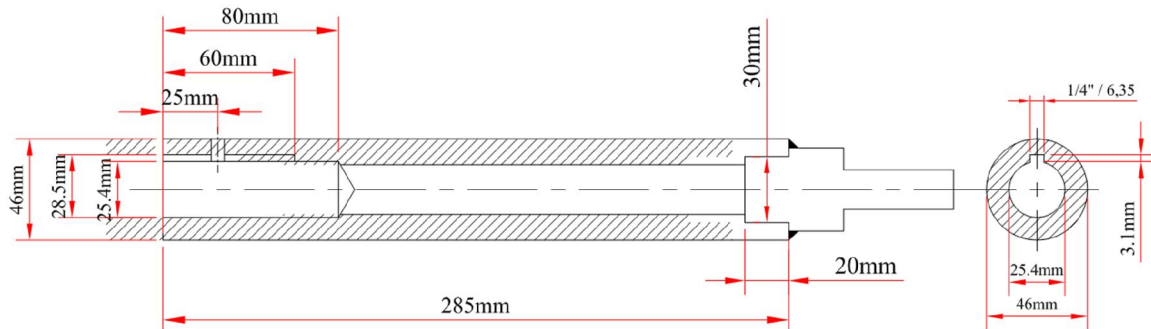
Adaptador utilizado para o acoplamento do motor hidráulico ao trado
